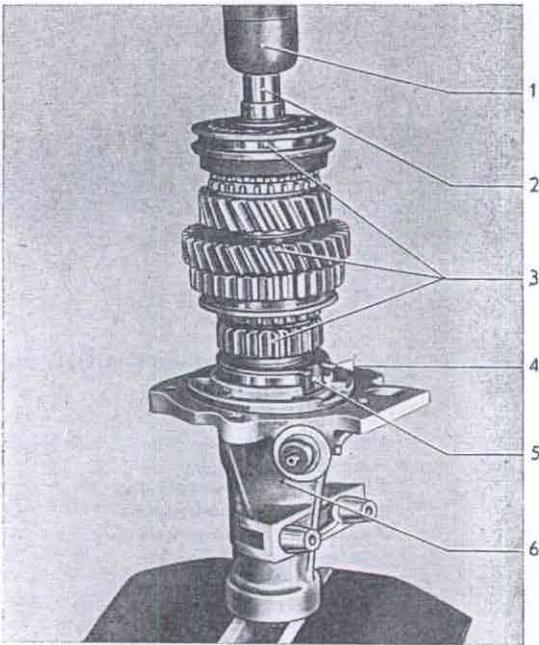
Hauptwellen-Zahnradblock in Getriebegehäuseverlängerung einschlagen
